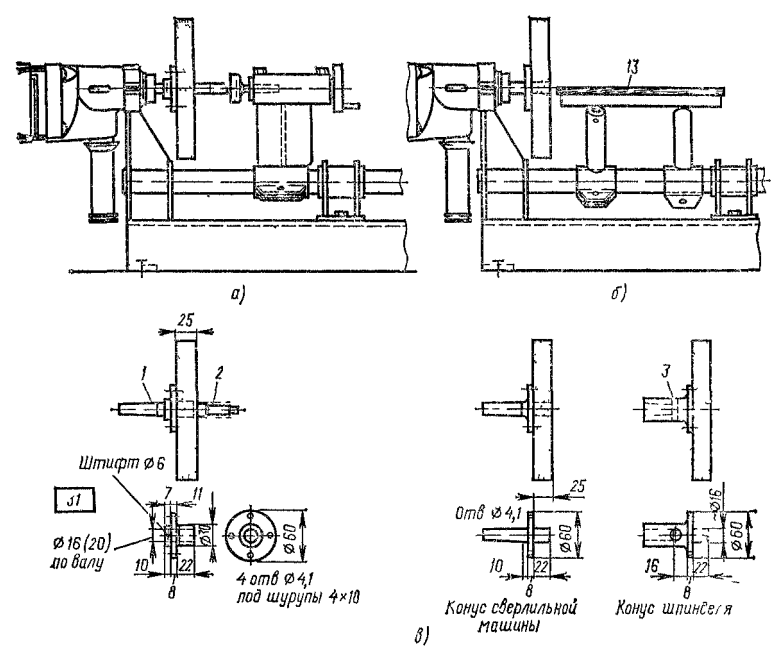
Круглошлифовальный станок по дереву (на базе станков рис. 135, 138 и 139):
